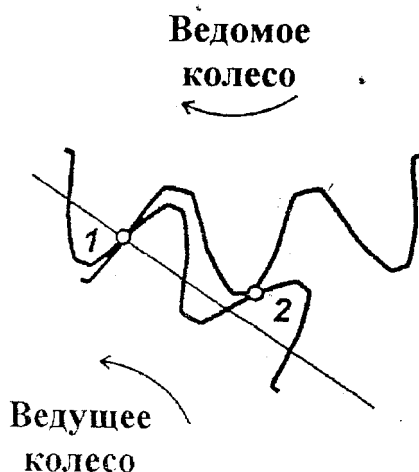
Схема зацепления геометрически точных зубчатых колес в фазе перезацепления под нагрузкой
